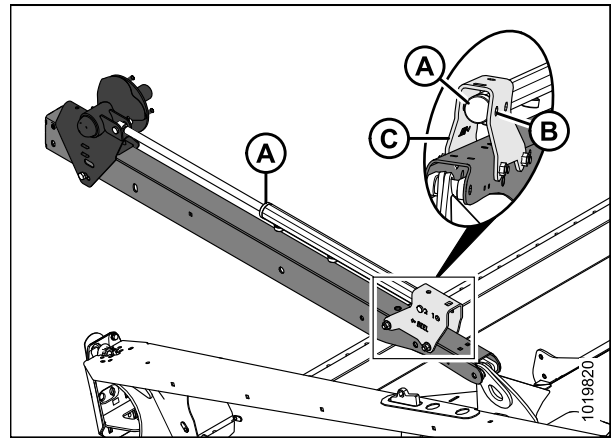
Linker Haspel-Horizontalzylinder
